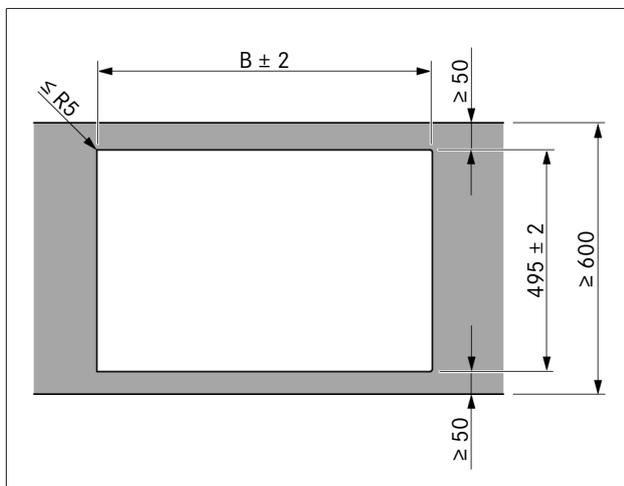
Ausschnittsmaße Aufsatzmontage
